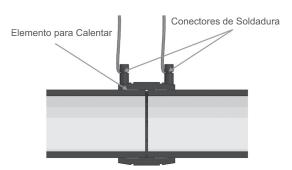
Detalles de la soldadura con electrofusión de los accesorios
